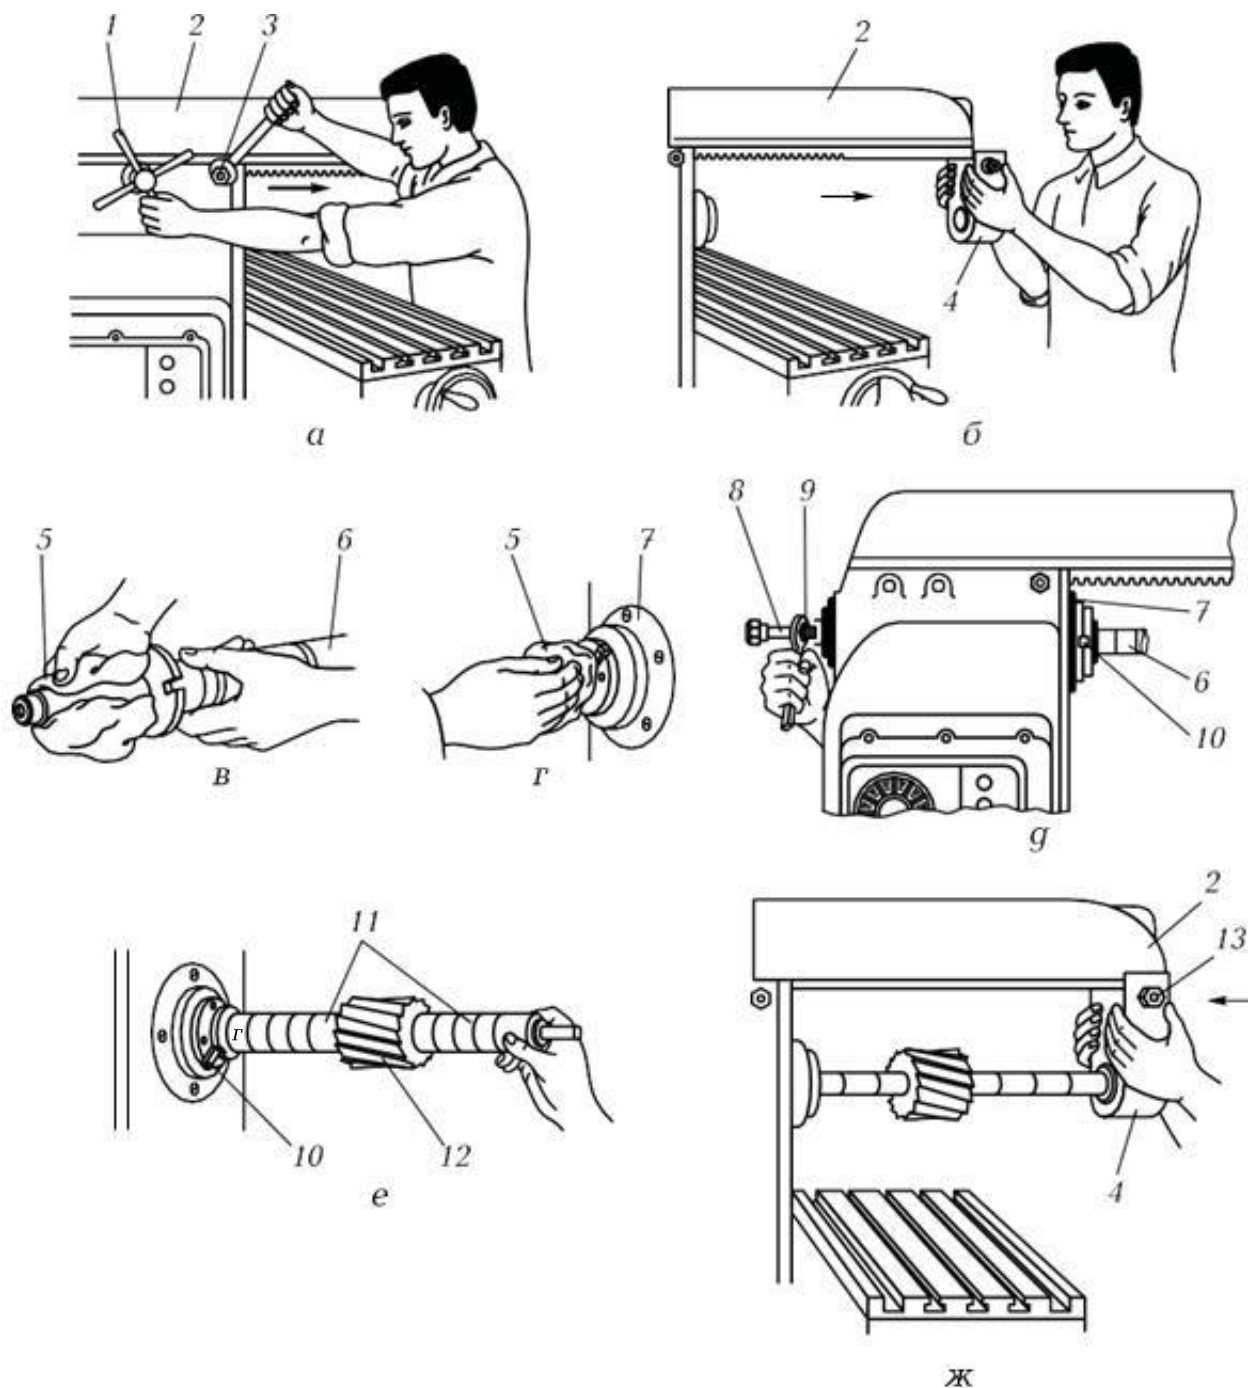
Последовательность установки и закрепления цилиндрической фрезы на горизонтально-фрезерном станке:
